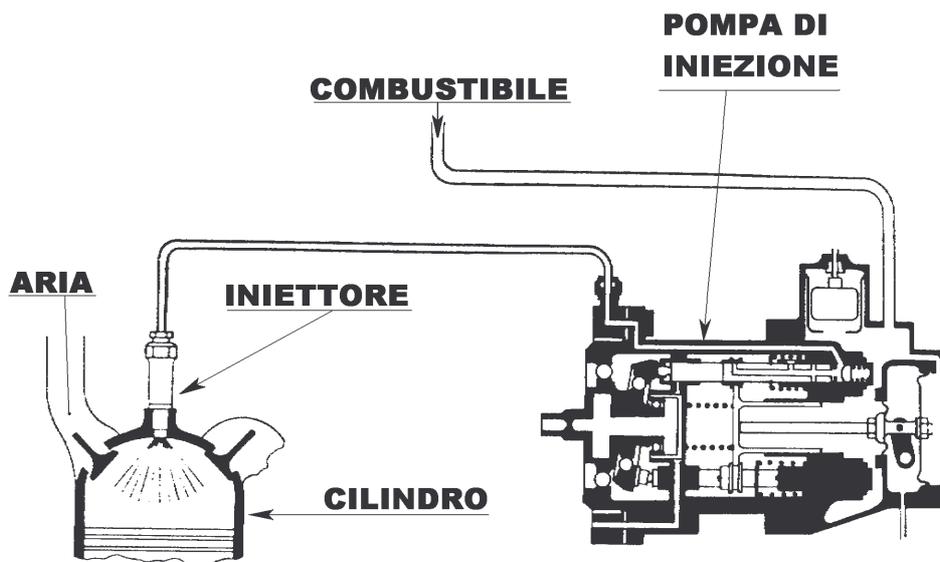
Circuito di iniezione con pompa Bosch per motore Diesel
